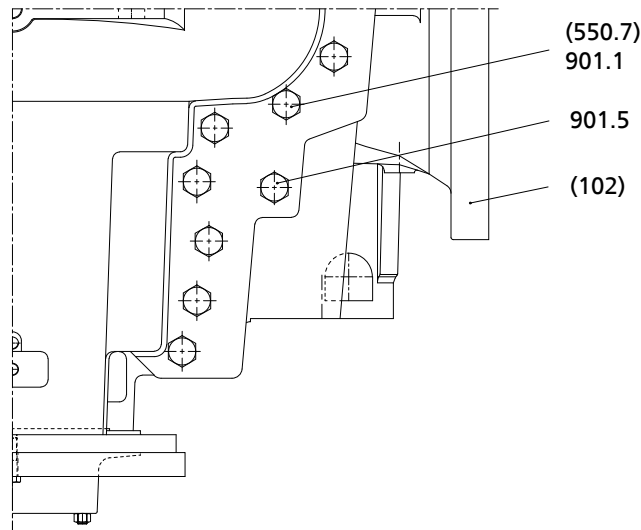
Деталировочный чертеж: Рабочее колесо с вращающимся кольцом
